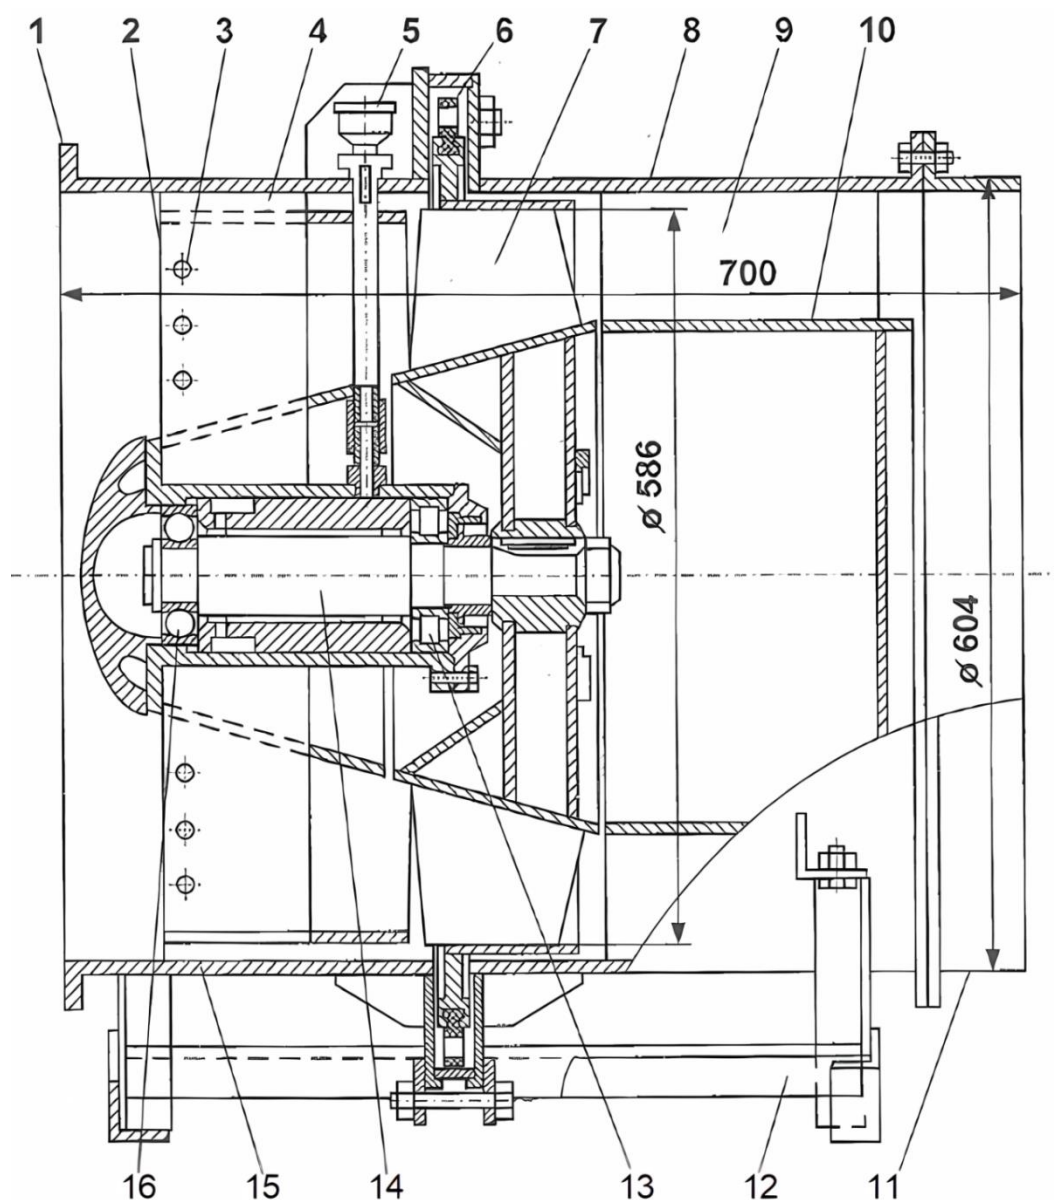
Вентилятор ВМП-6М: 1 и 11 — подводящий и отводящий патрубки; 2 — пластины растяжки; 3 — защитная решетка; 4 — противосрывное устройство; 5 — масленка; 6 — турбинное колесо; 7 — рабочее колесо; 8 и 15 — задняя и передняя части корпуса; 9 — спрямляющий аппарат; 10 — задний обтекатель; 12 — салазки; 13 и 16 — задний и передний подшипники; 14 — вал
